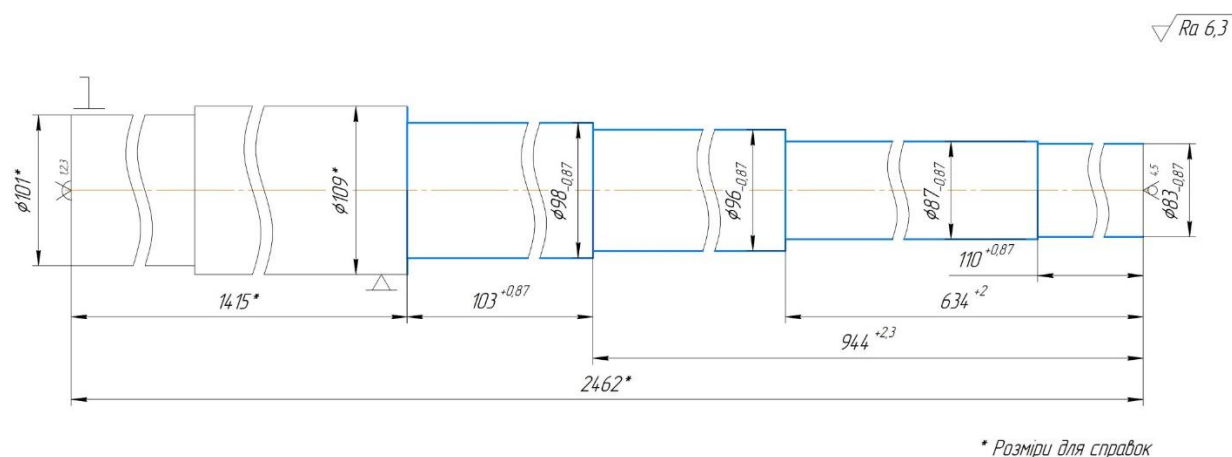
Схема базування і закріплення заготовки на токарній операції з ЧПК
